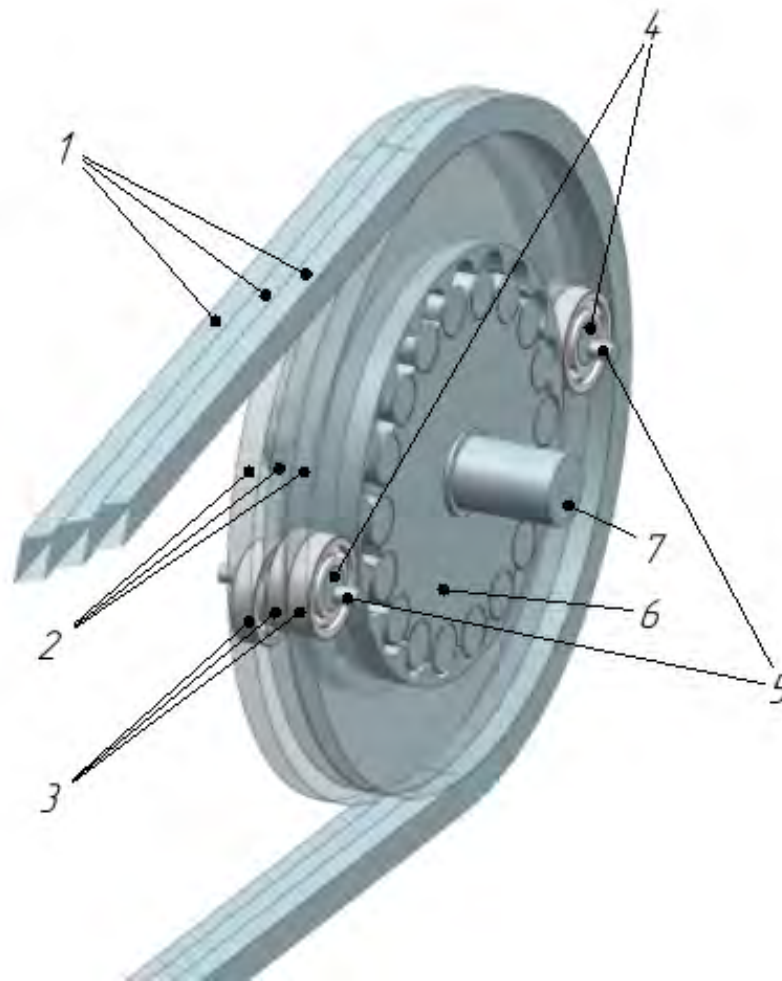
Схема взаимодействия элементов эксцентриковой передачи: 1 – ремень; 2 – сателлит; 3 – подшипник сателлита; 4 – эксцентрик сателлита; 5 – дополнительный вал сателлита; 6 – центральное колесо; 7 – выходной вал
